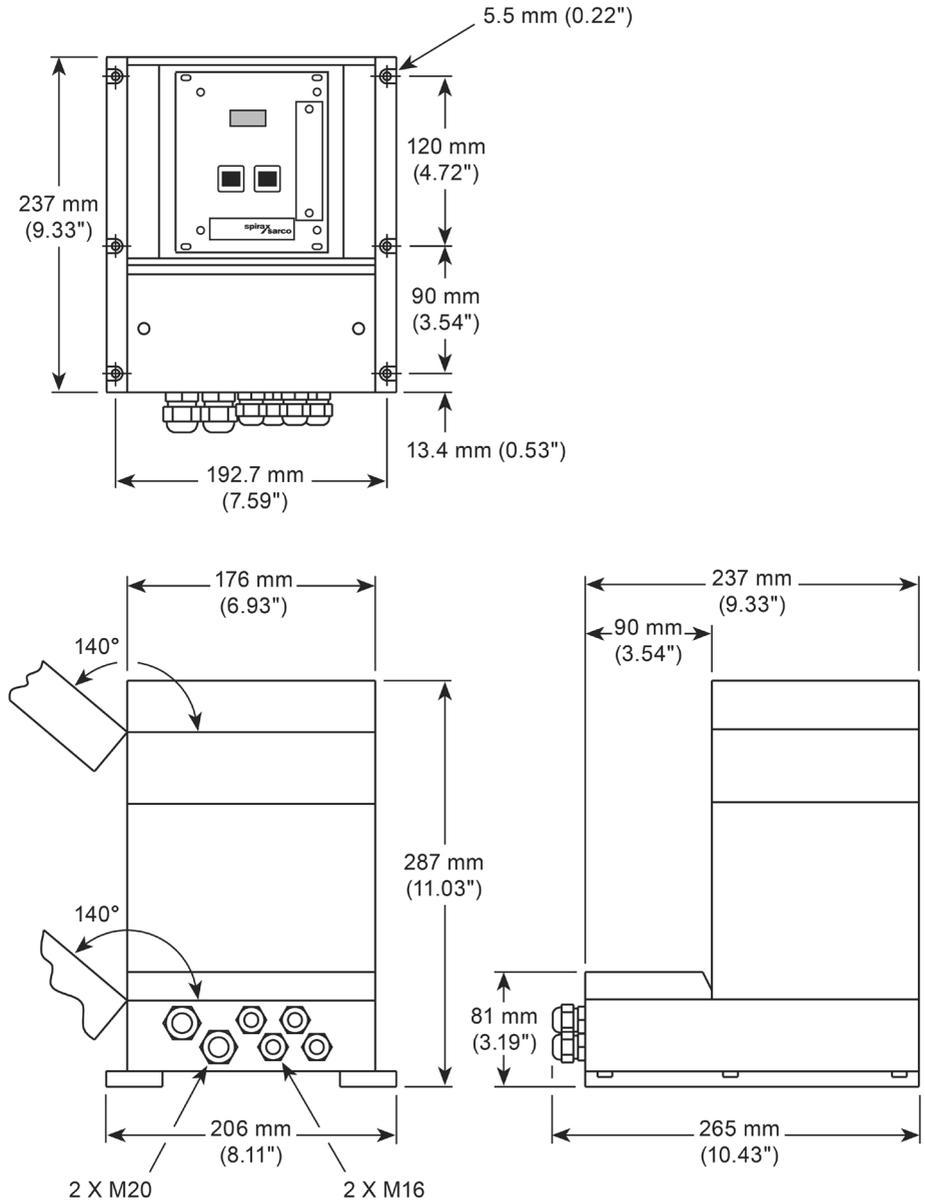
Dimensioni con custodia per montaggio a parete B19-21
